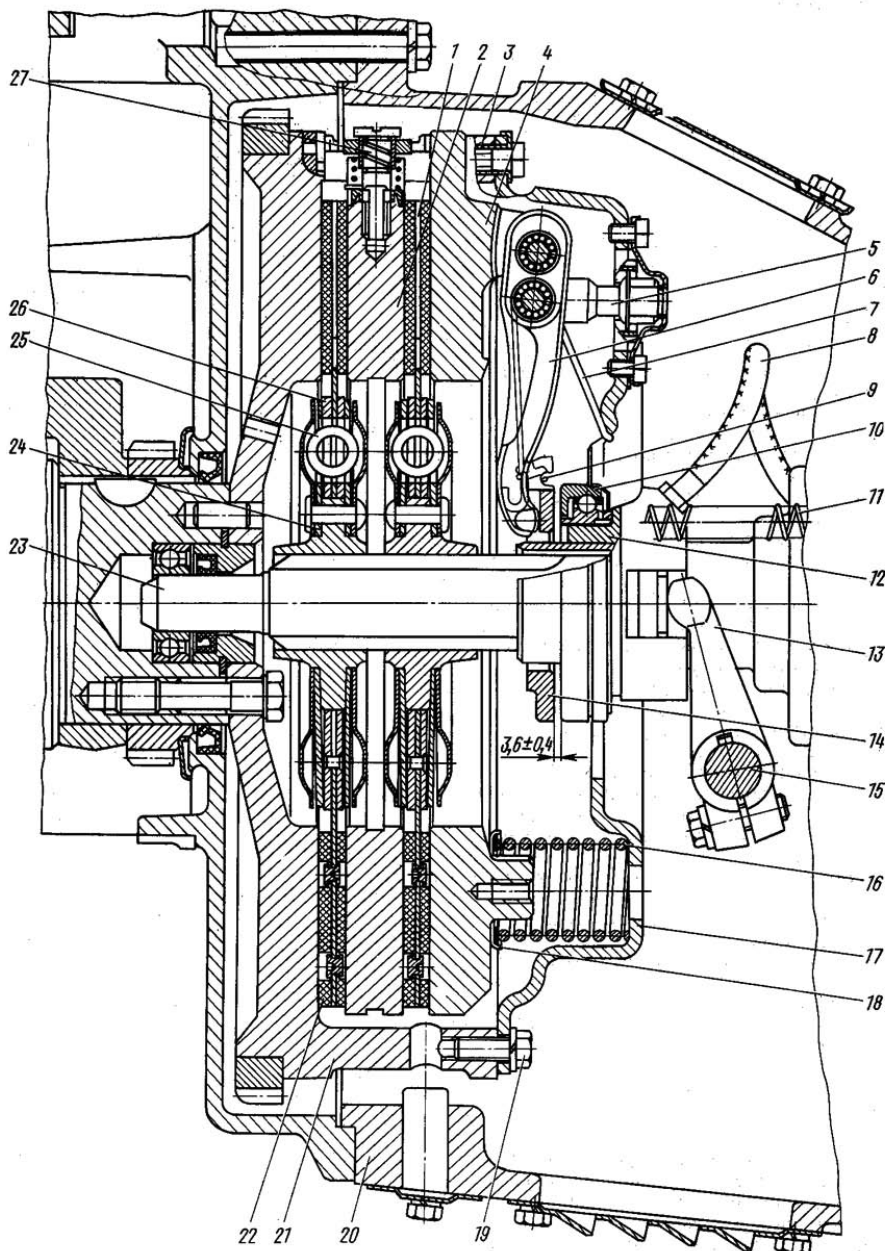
Сцепление: 1—ведомый диск; 2—средний ведущий диск; 3—установочная втулка; 4—нажимной диск; 5—вилка оттяжного рычага; 6—оттяжной рычаг; 7—пружина упорного кольца; 8—шланг смазки муфты; 9—петля пружины; 10—радиально-упорный подшипник выключения сцепления; 11—оттяжная пружина; 12—муфта выключения сцепления; 13—вилка выключения сцепления; 14—упорное кольцо; 15—вал вилки; 16—нажимная пружина; 17—кожух сцепления; 18—теплоизолирующая шайба; 19—болт крепления кожуха; 20—картер сцепления; 21—маховик; 22—фрикционная накладка; 23—первичный вал коробки передач; 24—диск гасителя крутильных колебаний; 25—пружина гасителя крутильных колебаний; 26—кольцо ведомого диска; 27—механизм автоматической регулировки положения среднего ведущего диска
